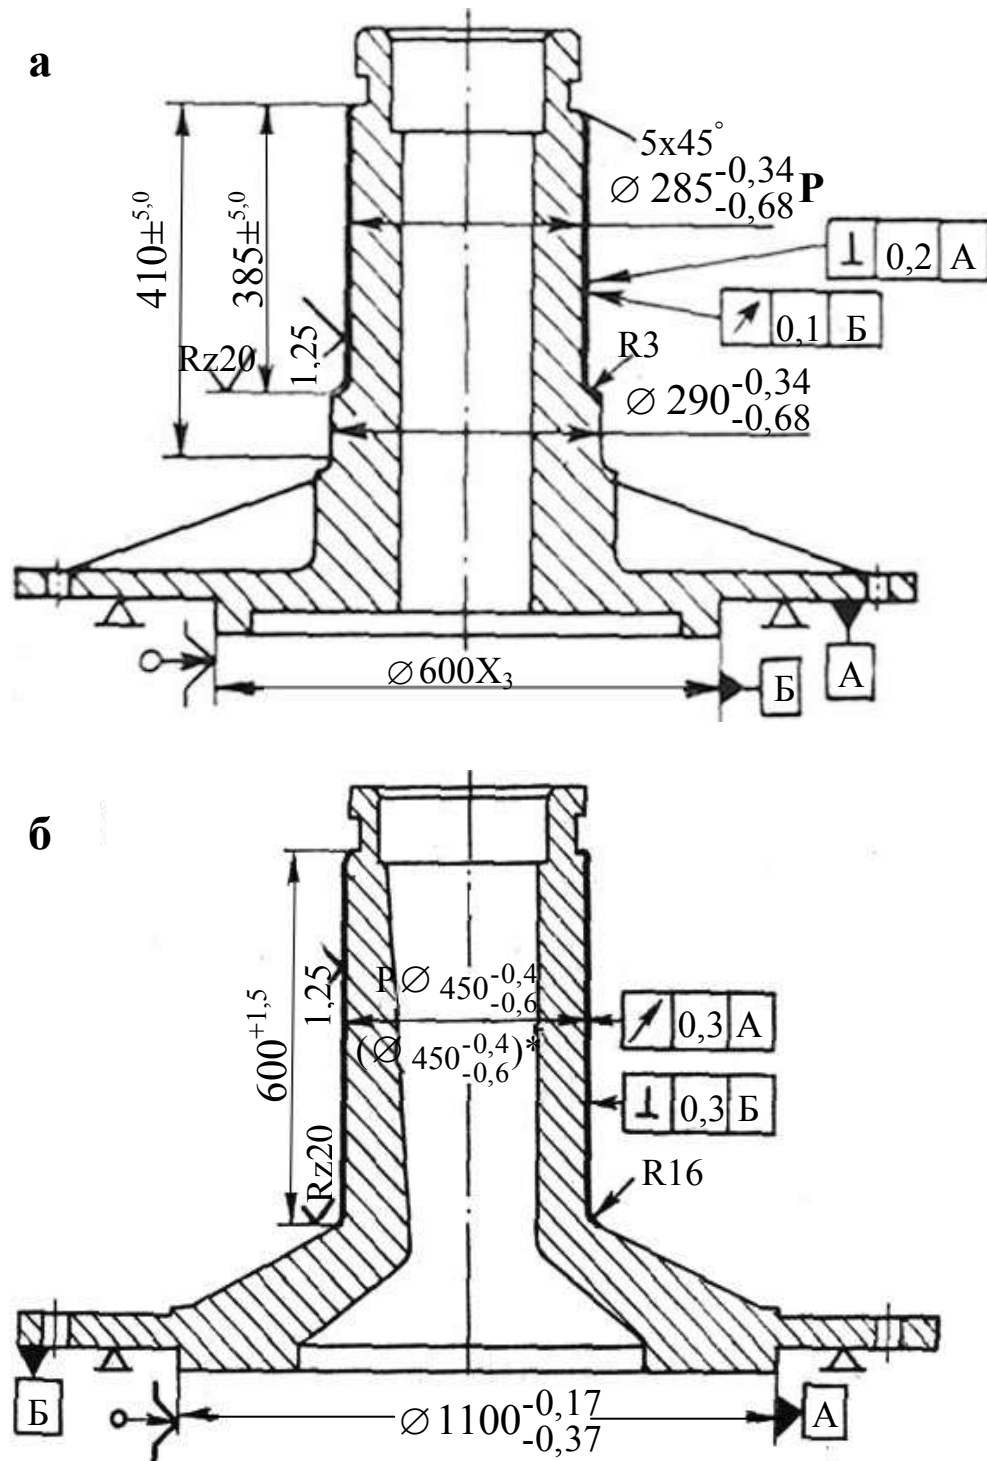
Ремонтные чертежи центральной цапфы для различных экскаваторов: * – размер исходный по чертежу
